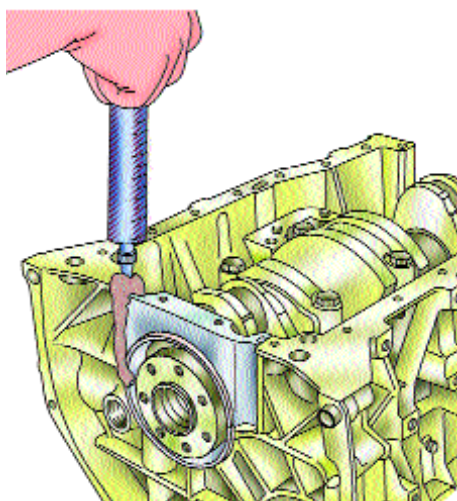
Герметизация крышки 1-го коренного подшипника коленчатого вала двигателя F3R 272
